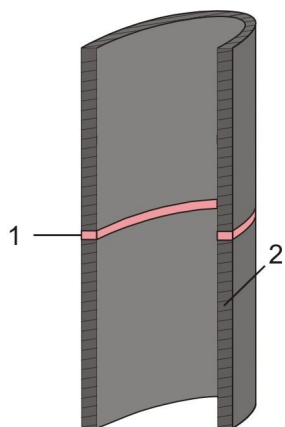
Предлагаемая конструкция обсадной металлической колонны (в разрезе):
